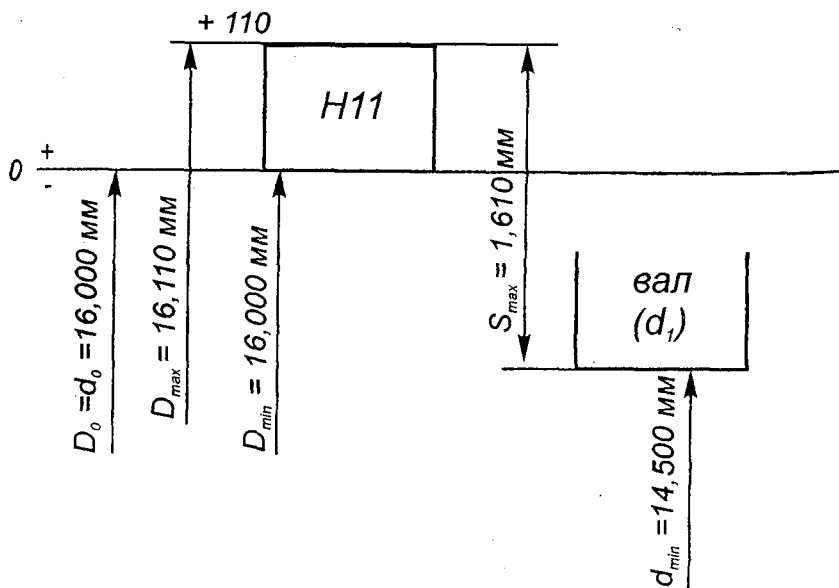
Схема расположения полей допусков шлицевого соединения по внутреннему диаметру
